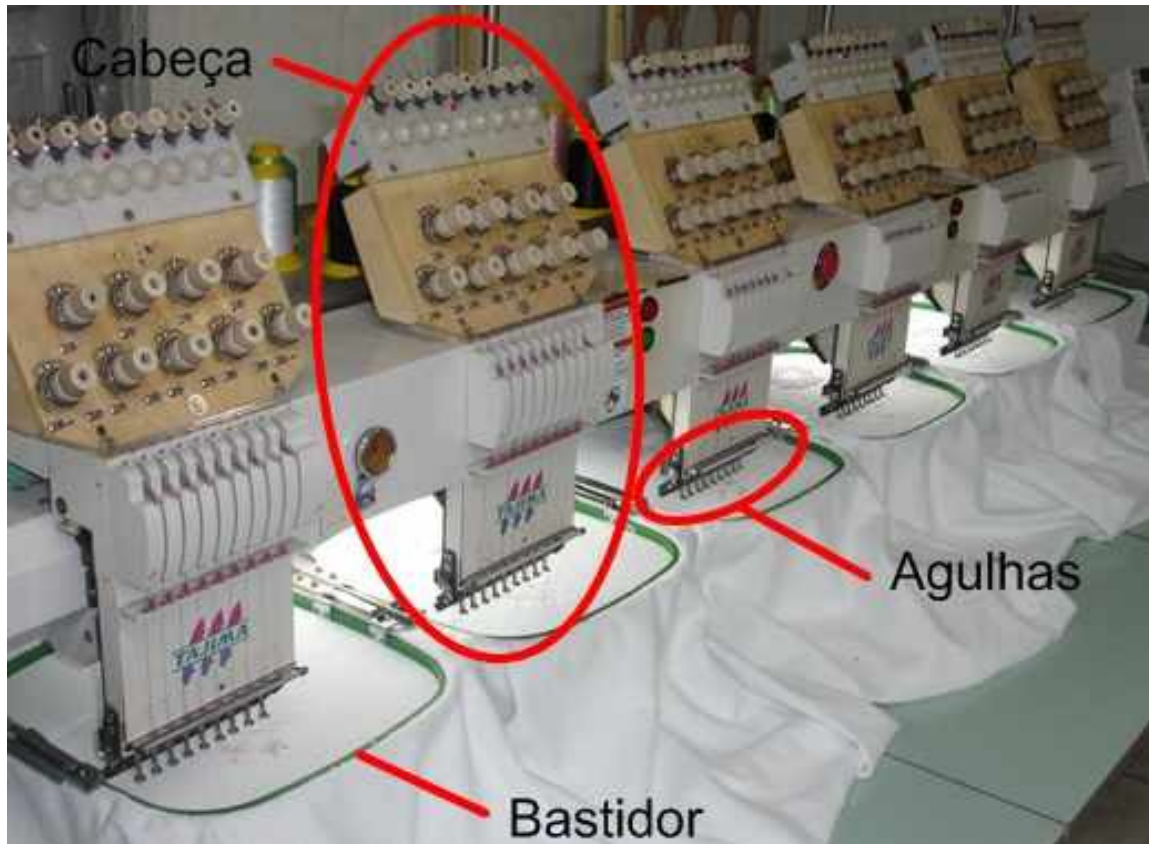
Máquina de Bordar C6 (Cilíndrica 6).
